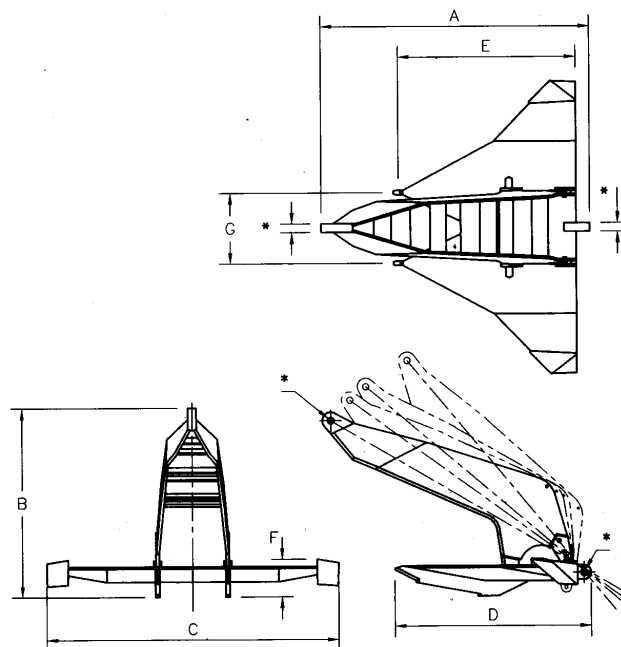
Bruce FFTS-PM [BRUCE ANCHOR GROUP]
